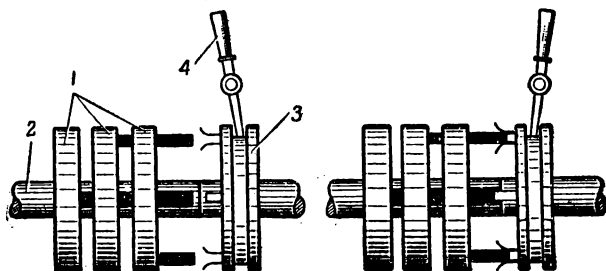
Приспособление для замыкания обмотки ротора накоротко:
